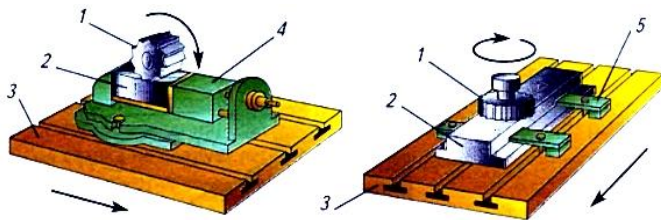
Фрезерование плоскостей: а — цилиндрической фрезой в тисках; б — торцевой фрезой на столе станка: 1 — фреза; 2 — заготовка; 3 — стол; 4 — тиски; 5 — прижим
